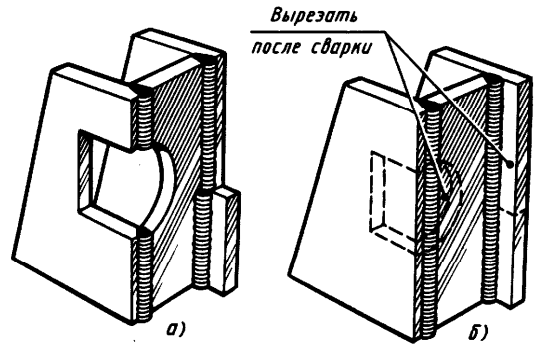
Сварная конструкция с прерывистыми швами: а - неудобными для электрошлаковой сварки; б - удобными
